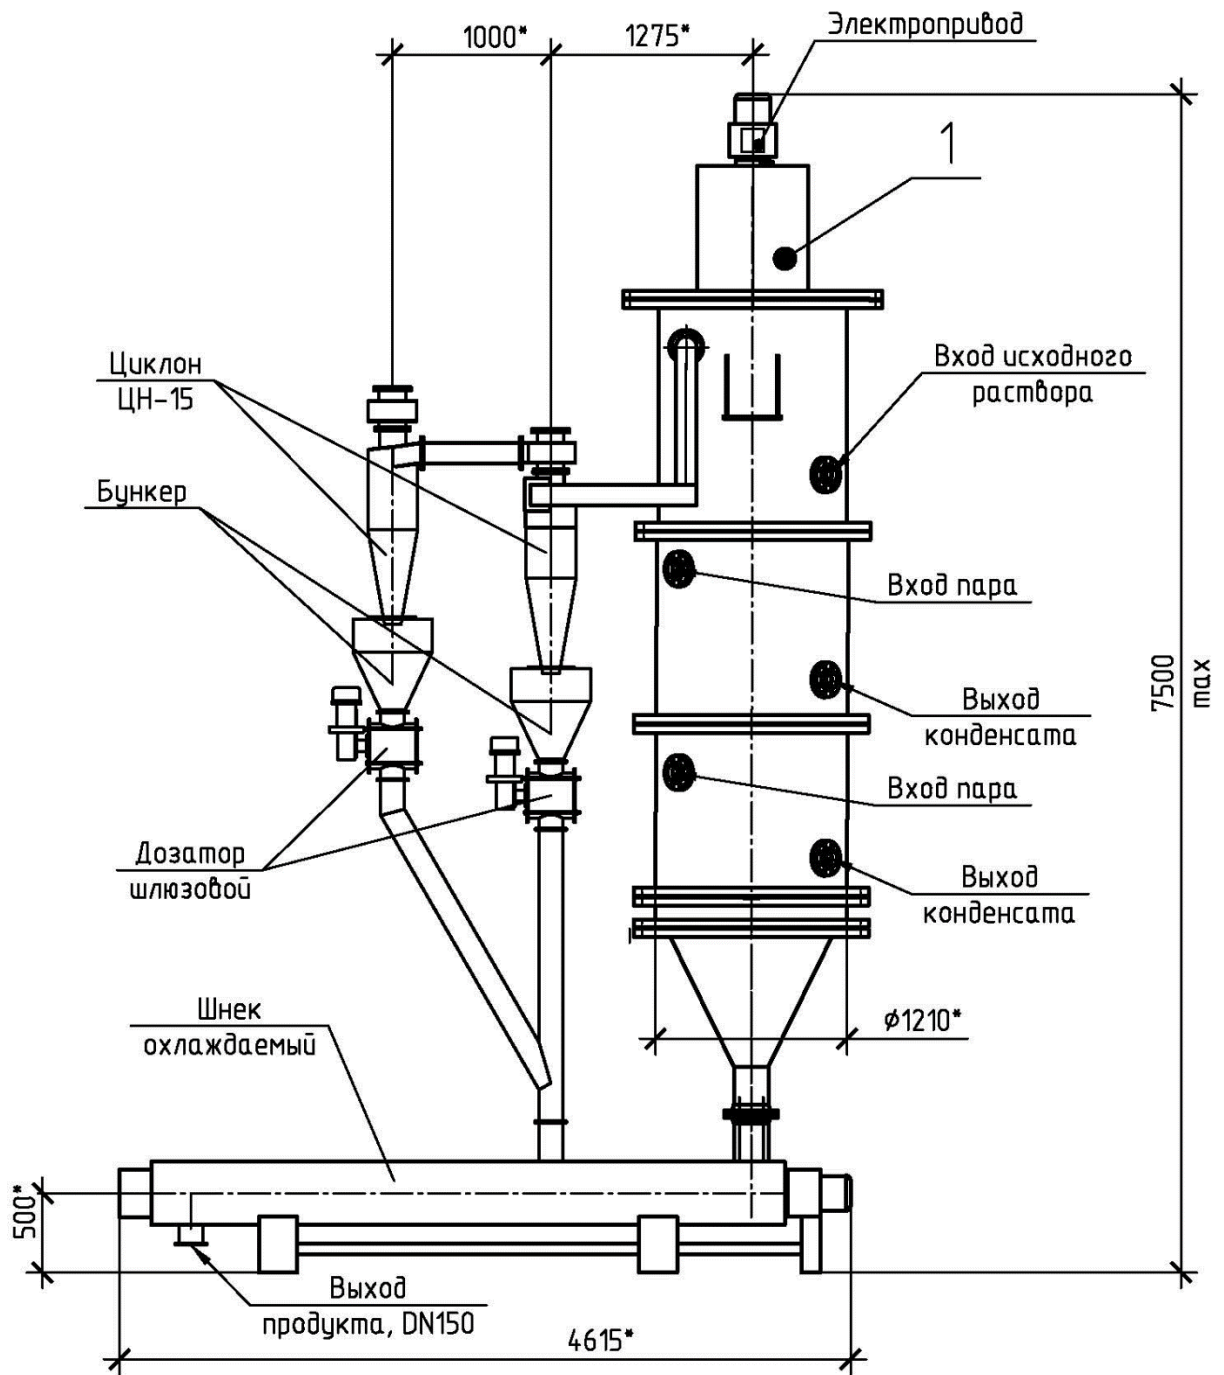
Габаритные размеры установки сушки. *Размеры для справок
